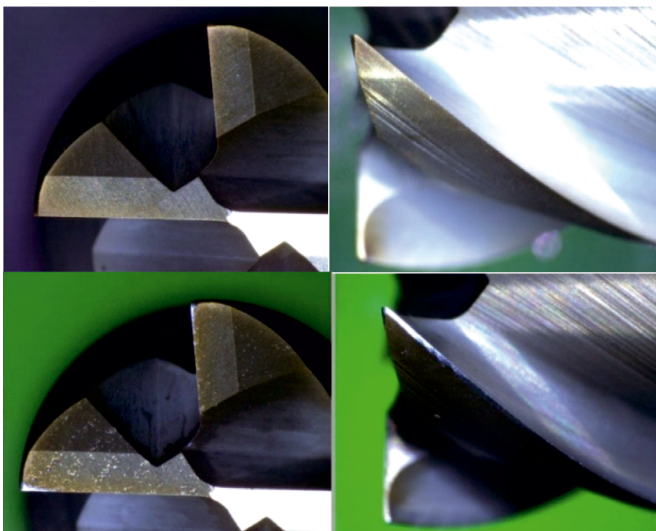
Фреза JJ Tools 4SUE080120S08:
